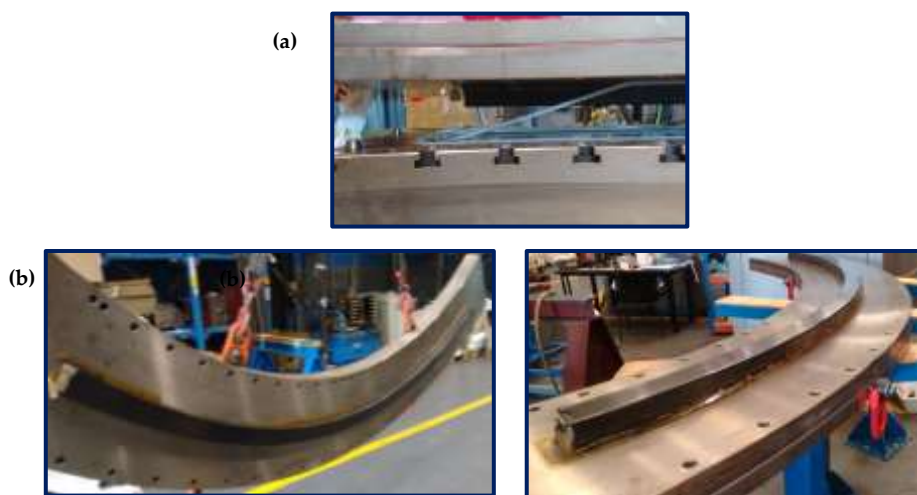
(a) Apertura del molde en caliente a 180 ± 5 °C y (b) pieza en convexo de aluminio para ser desmoldeada.
